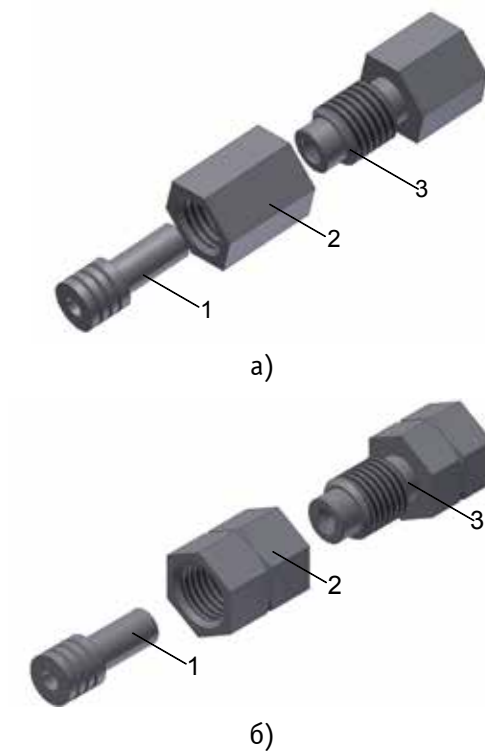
Приспособление для монтажа блочных резьбовых соединителей типа розетка в тракте 3,5/1,52 мм в метрическом (ЖНКЮ.296371.030, рис. а) и дюймовом (ЖНКЮ.296371.030-01, рис. б) исполнениях
